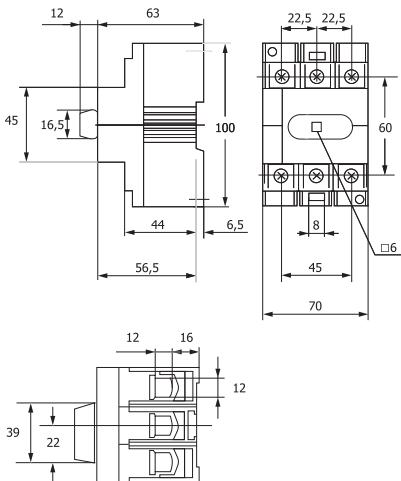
Габаритные и установочные размеры рубильников 100-125А 3Р
